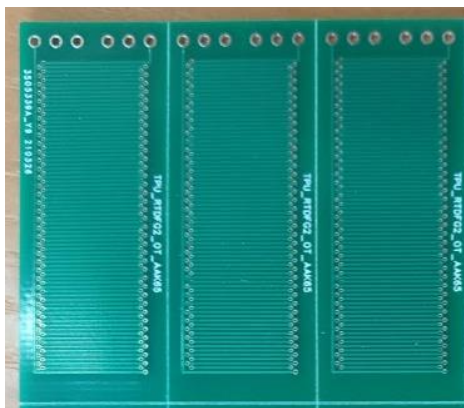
Изготовленный образец 3 RTD-феррозонда
